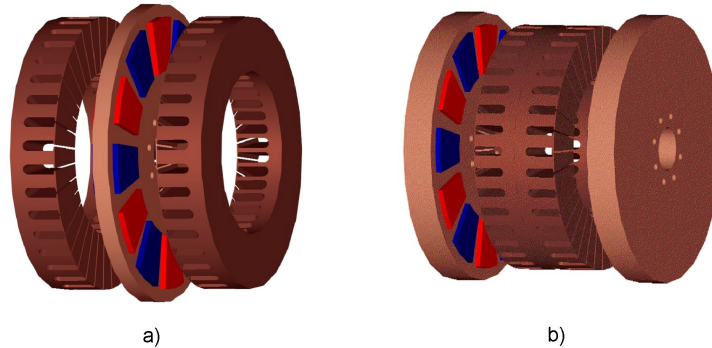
Configuraciones de máquina axial de doble cara con estátor ranurado: a) Rotor interno; b) Estátor interno
